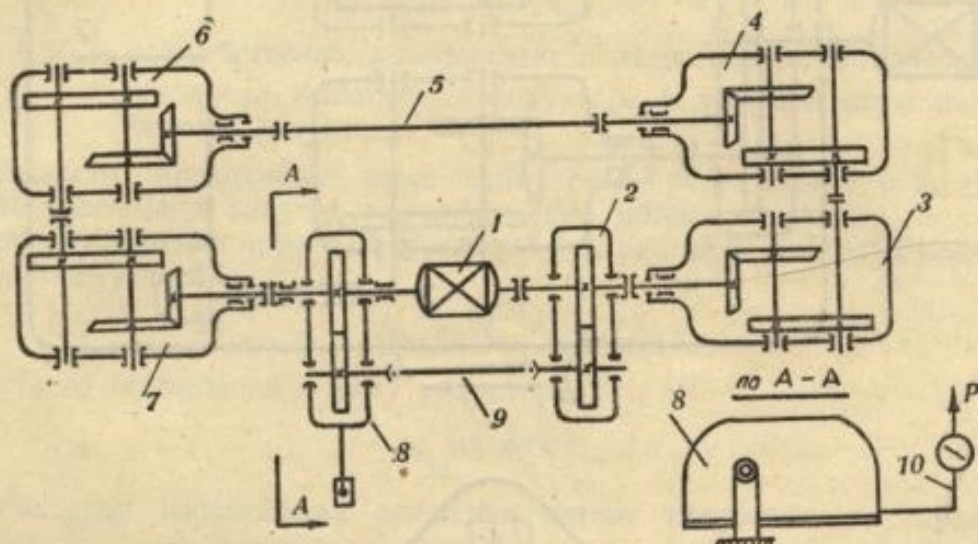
1 — Электродвигатель, 2 — цилиндрический редуктор, 8 — цилиндрический качающийся редуктор, 3, 4, 6, 7 — испытуемые редукторы, 5 — гибкий вал, 9 — карданный вал, 10 — динамометр.
